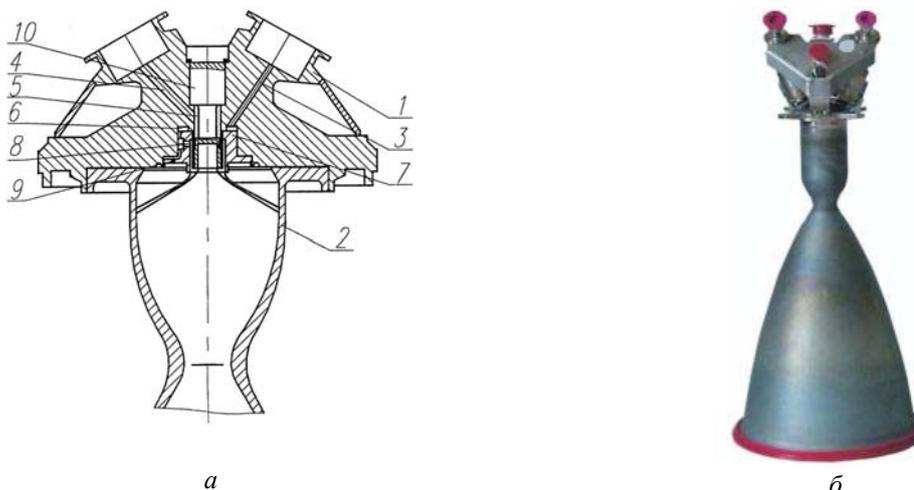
Двухкомпонентный ракетный двигатель малой тяги 11Д458Ф:
